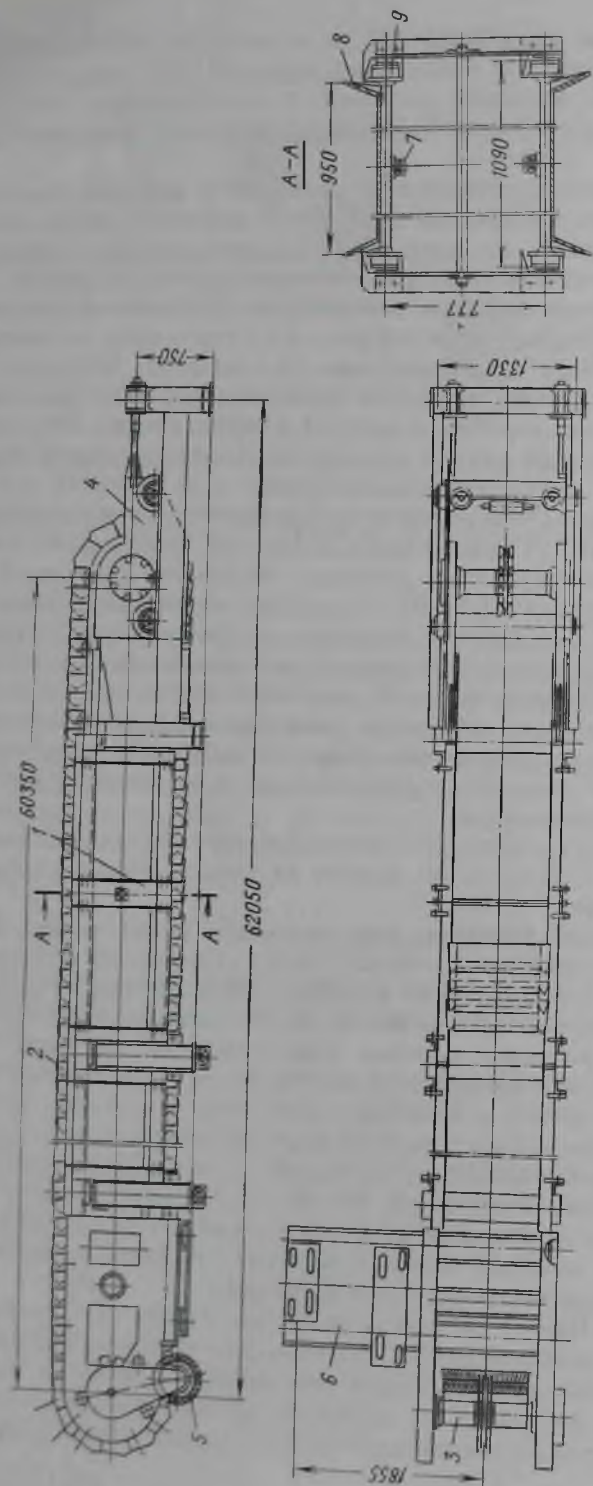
Пластинчатый конвейер КФР-1: 1 — рама става; 2 — несущее полотно; 3 — приводная и 4 — натяжная станции; 5 — устройство для очистки штабы; 6 — штаба; 7 — тяговая цепь; 8 — пластина; 9 — ходовые ролики
